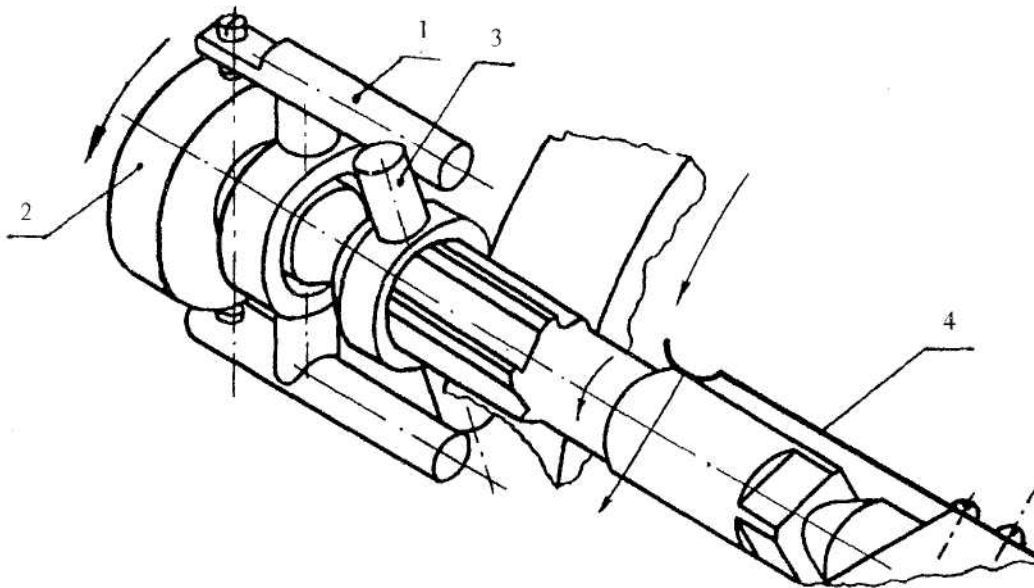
Чистомоментний диференціальний привод обертання розвертки
